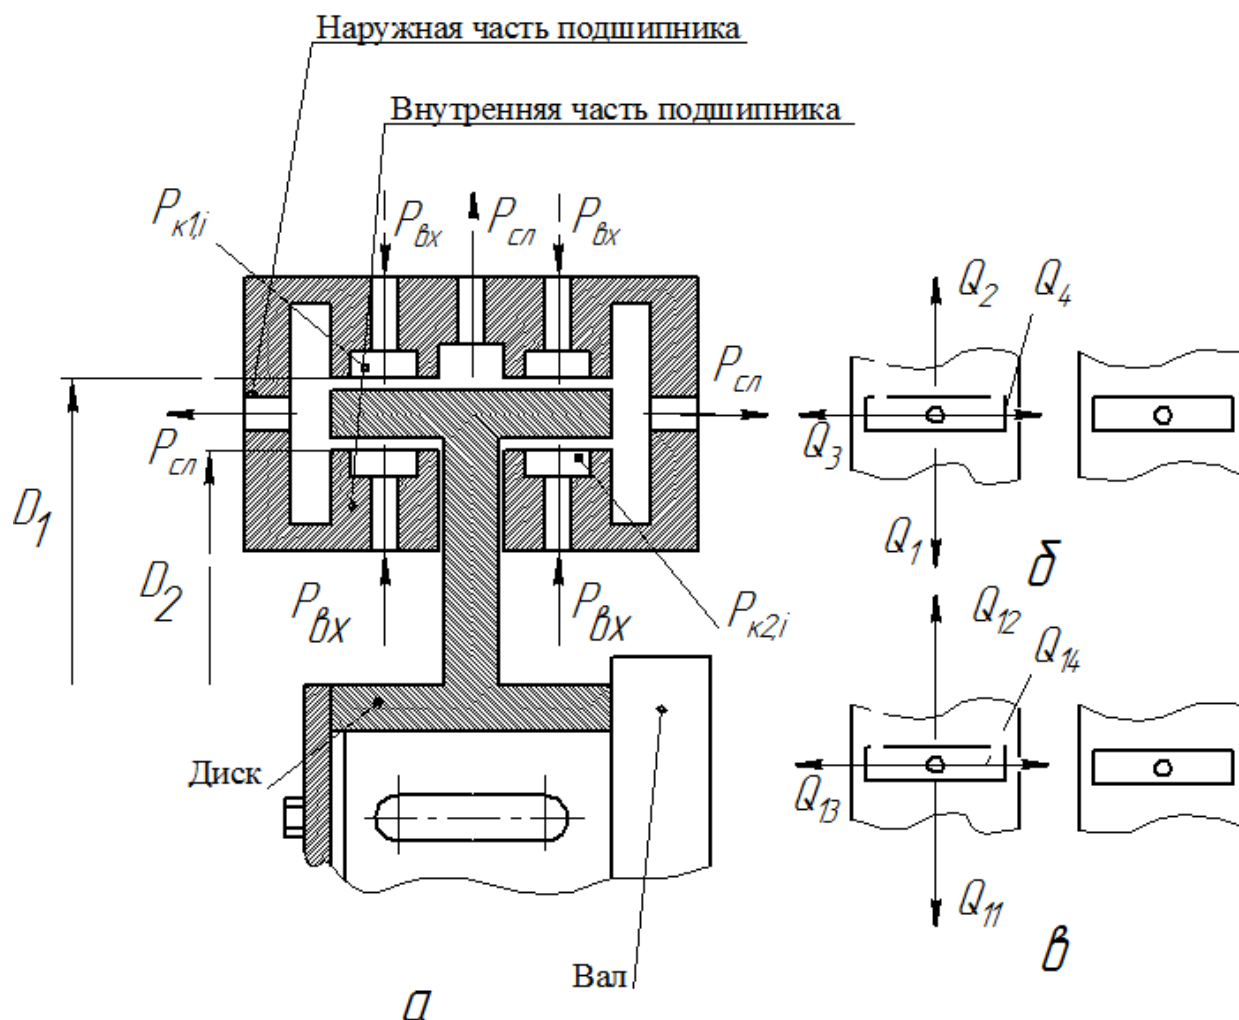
Схема подшипника (а) и развертки наружной (б) и внутренней (в) рабочих поверхностей подшипника
